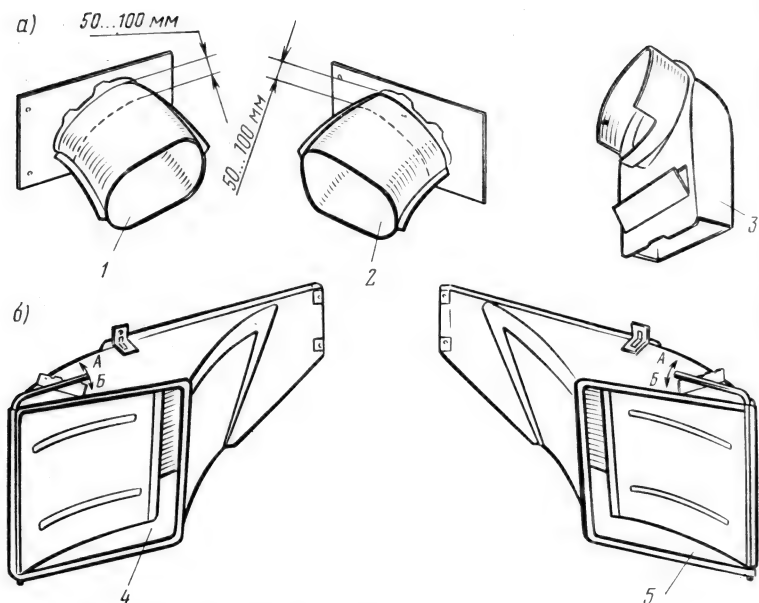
Воздухопритоки моторного отсека автомобиля до переделки (а) и после (б); заводские обозначения деталей: 1 — 966-5629014; 2 — 966-5629015; 3 — 966-1300010; 4 — 966-5629021Б; 5 — 5629020Б; А — положение "Лето"; Б — положение "Зима"
